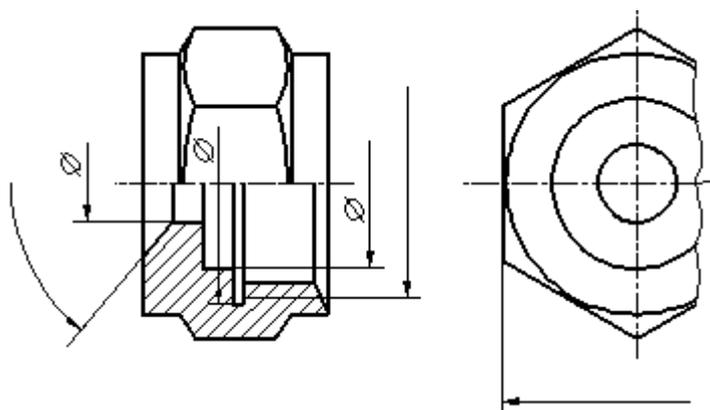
Пример нанесения размера с обрывом размерной линии
